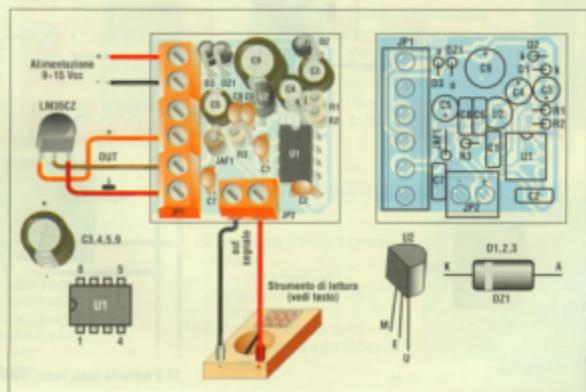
Collegamento della sonda e sua impermeabilizzazione.
